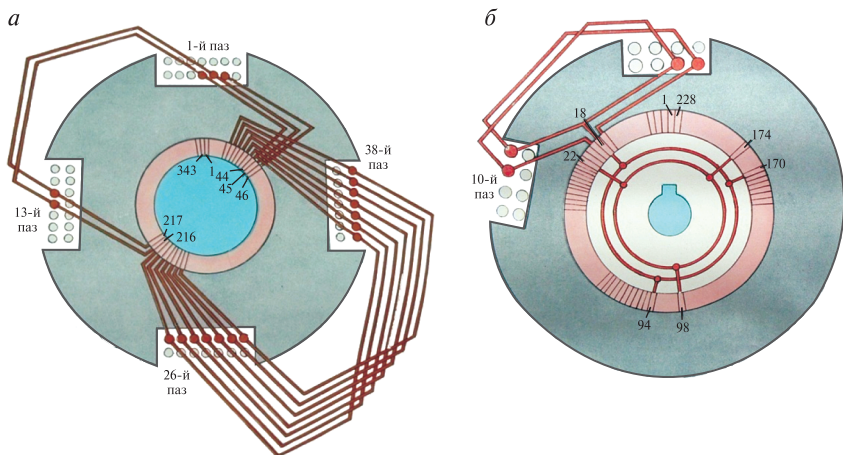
Схема соединения уравнивателей и катушек якоря с коллекторными пластинами генератора преобразователя (а) и с коллекторными пластинами двигателя преобразователя (б)
